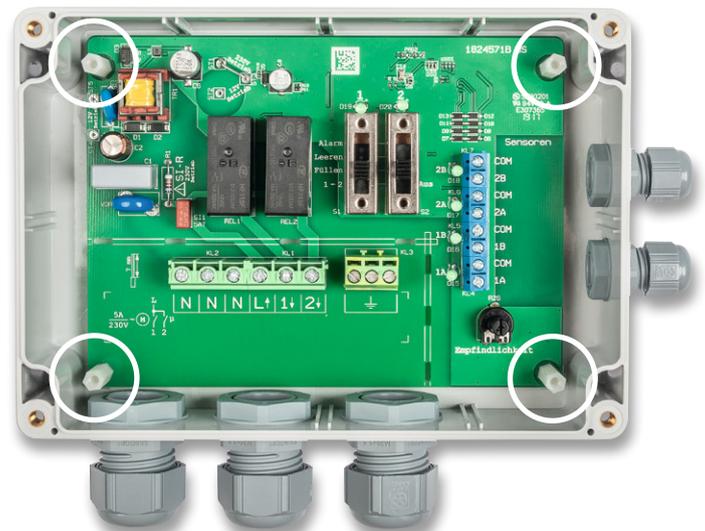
Die Platine wird mit vier Gewindebolzen im Gehäuse befestigt.
